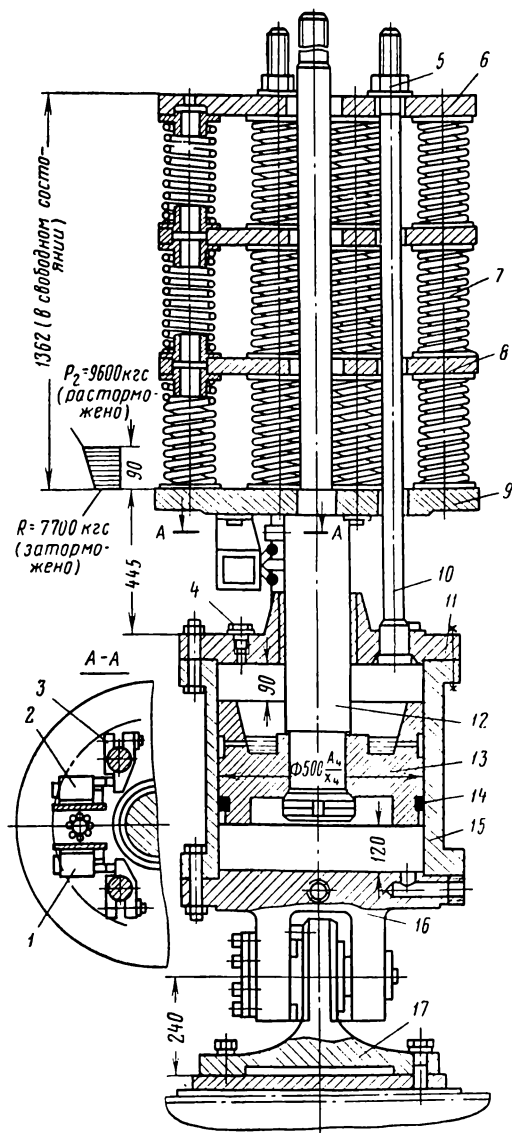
Пружинный пневматический привод тормоза машины ЦШ5×8
